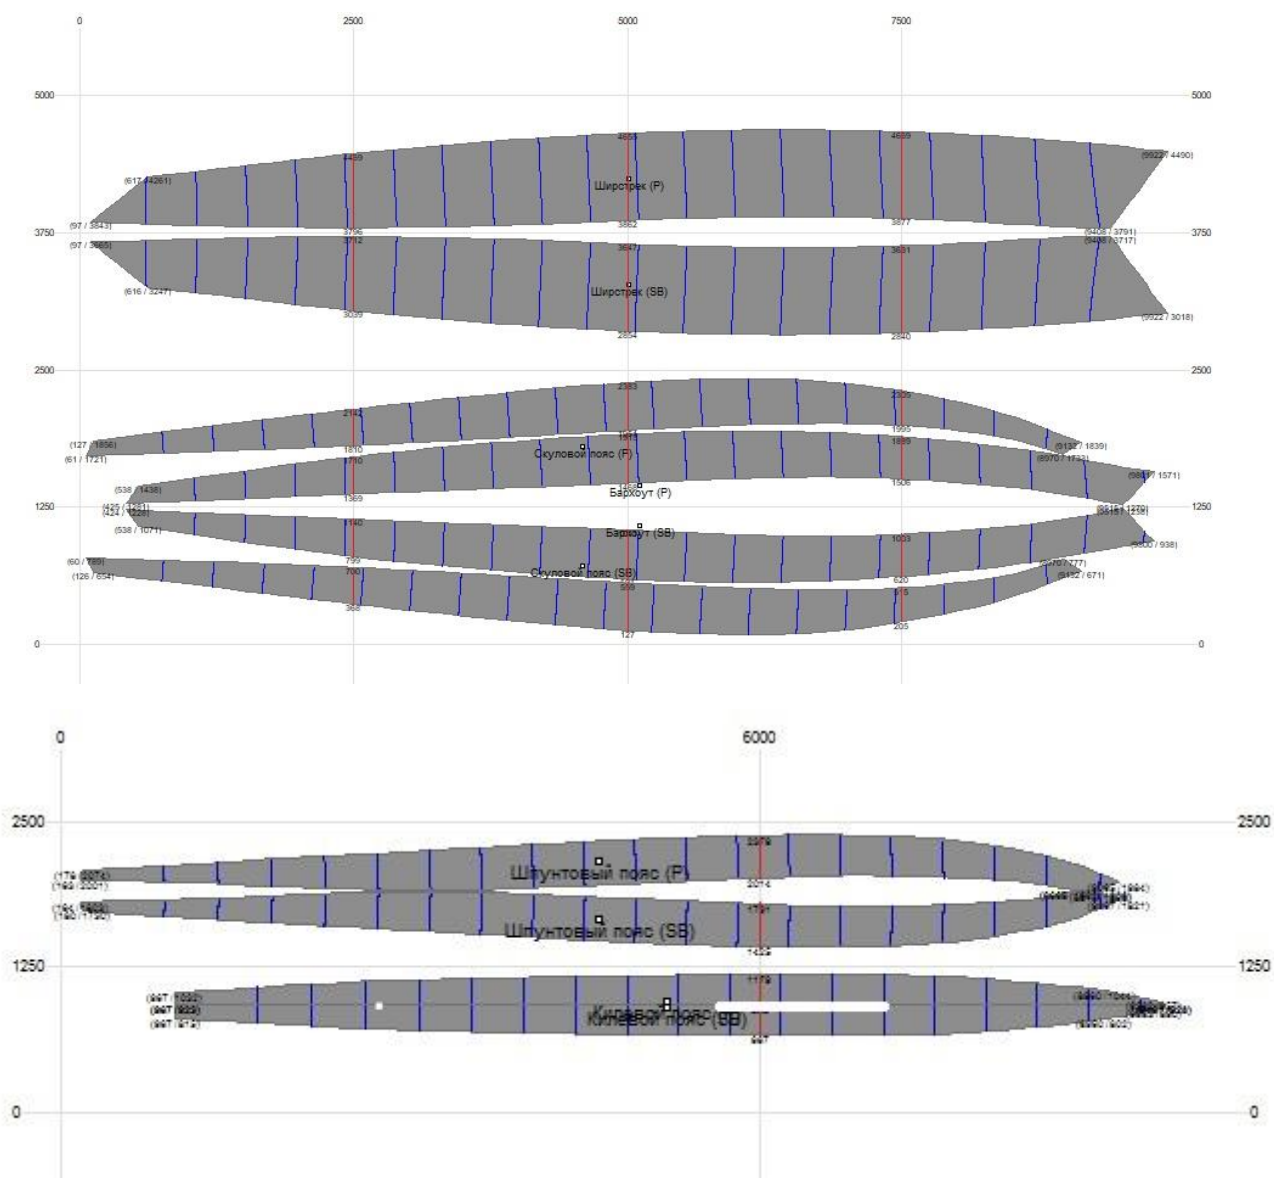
Развертки и раскрой листов обшивки корпуса парусной яхты
